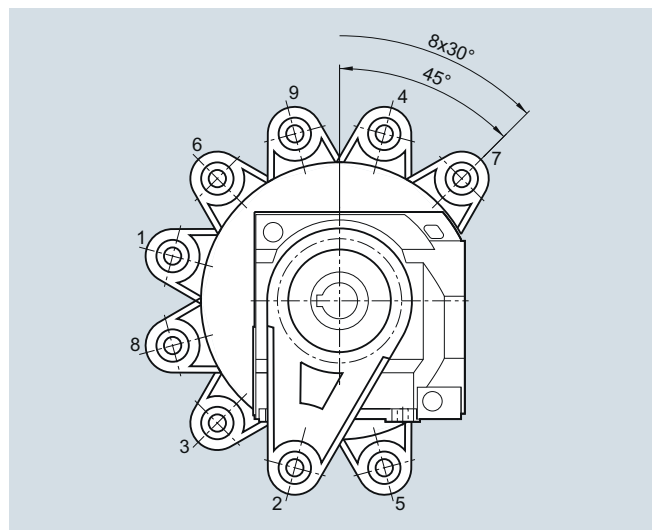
/12 Stirnradschneckengetriebe CAD, Figur 2 Baugröße 39 bis 89
